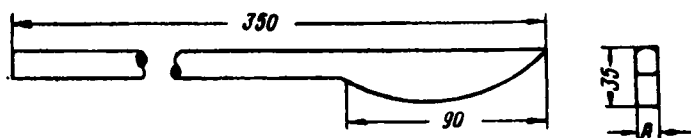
Рычаг для подъема секций якоря из паза. Размер А принимается равным ширине паза
